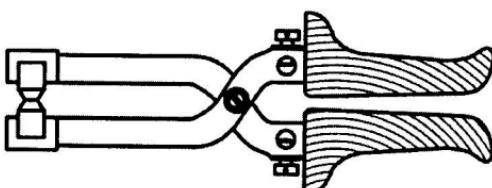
Кліщі Бенардоса для контактного зварювання
